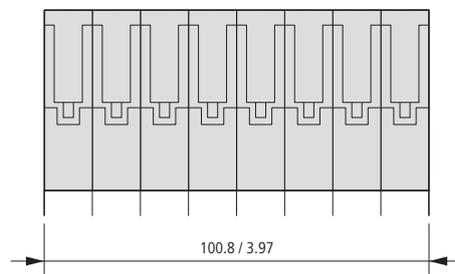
Rückansicht Elektronikmodul in Blockausführung
